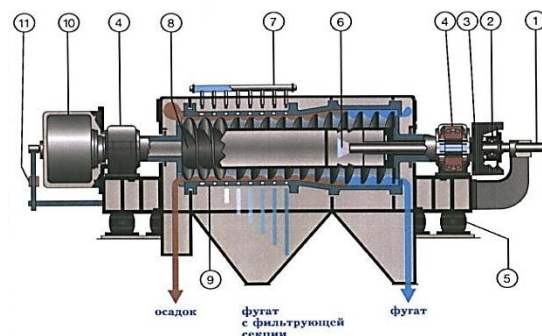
Схема устройства осадительно-фильтрующей центрифуги [34]: 1 – питающая труба; 2 – упорные подшипники; 3 – ведомый шкив; 4 – главные подшипники; 5 – амортизаторы; 6 – питающая камера; 7 – система брызгал для промывки фильтрующей секции; 8 – шнек; 9 – фильтрующая секция; 10 – планетарный редуктор; 11 – датчик крутящего момента
